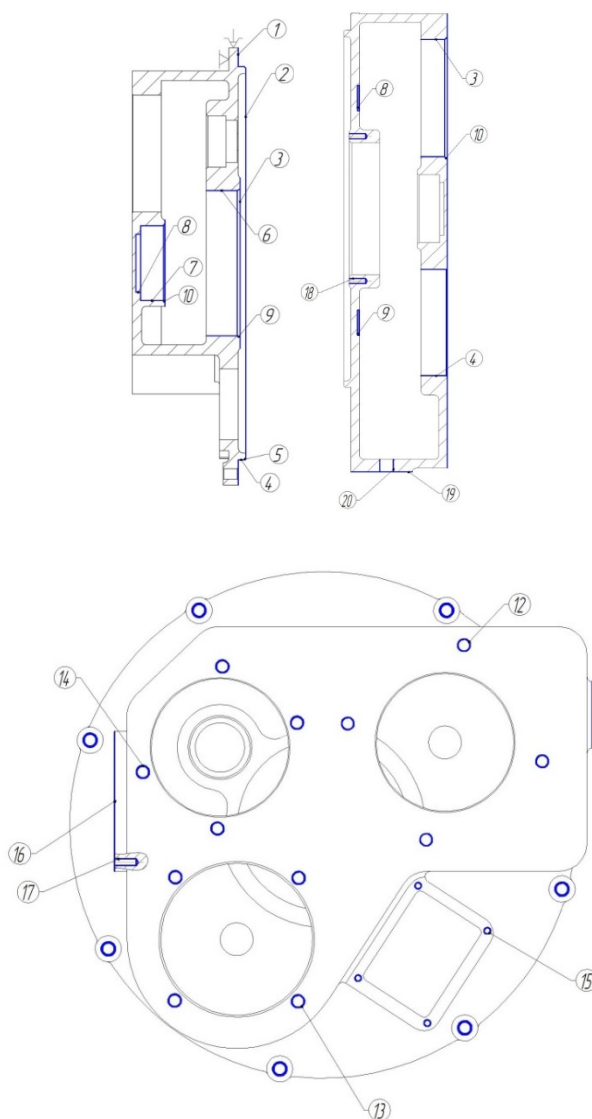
Поверхности детали «Корпус редуктора погрузчика»
